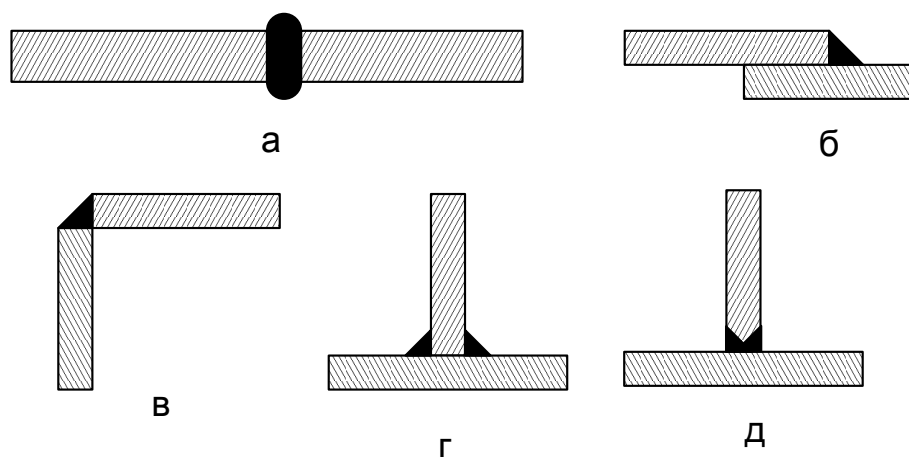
Виды сварных швов и соединений
